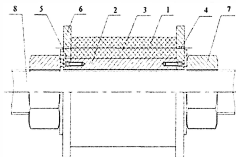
Схема размещения термопары в малоразмерной заготовке детали:
